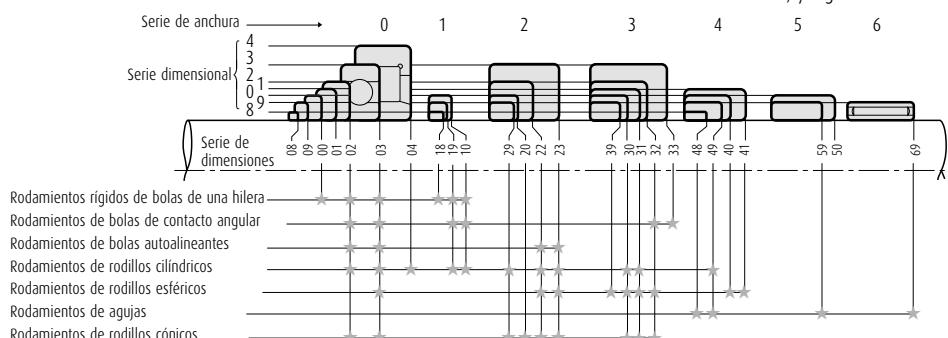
Series de dimensiones de los rodamientos radiales
